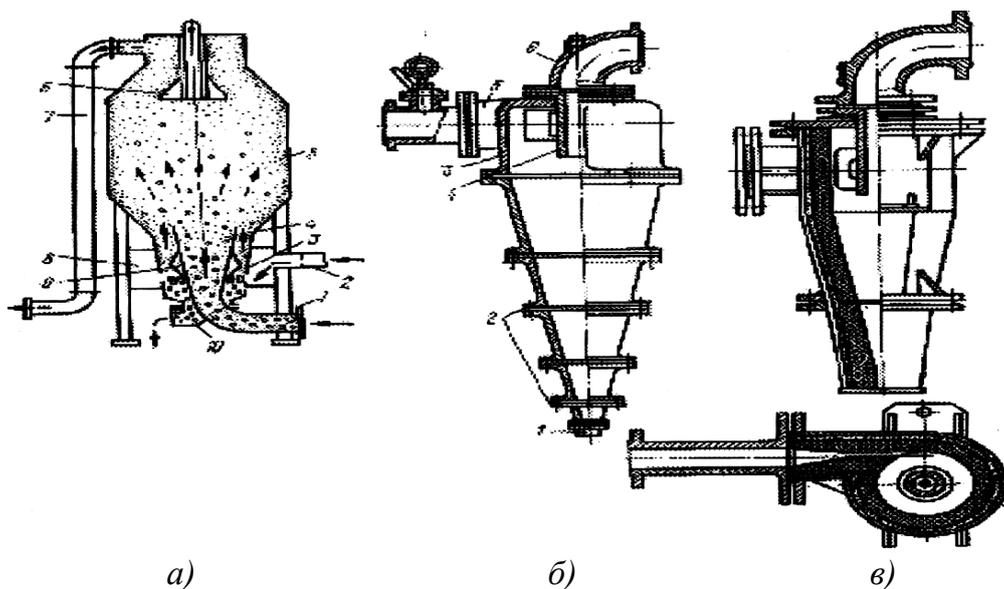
Гидравлические классификаторы: а – прямоточный: 1, 2, 7, 10 – трубы; 3 – классификационная камера; 4 – патрубок; 5 – осадительная камера; 6 – отбойный щиток; 8 – кольцевой коллектор; 9 – спиральные лопатки; б – сборный циклонный: 1 – отверстие; 2 – конические секции; 3 – цилиндрический корпус; 4 – центральная труба; 5 – подводный патрубок; 6 – отводящий патрубок; 7 – разгрузочный патрубок; в – гидроциклон сварной футерованный
